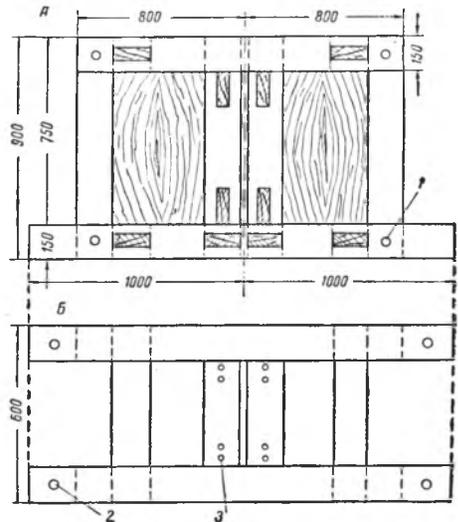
Станина круглопильного станка с подвижной кареткой: А — вид сбоку на станину без каретки; Б — вид на станину сверху. 1 — стяжной болт; 2 — болты фундамента; 3 — отверстия для крепления.
